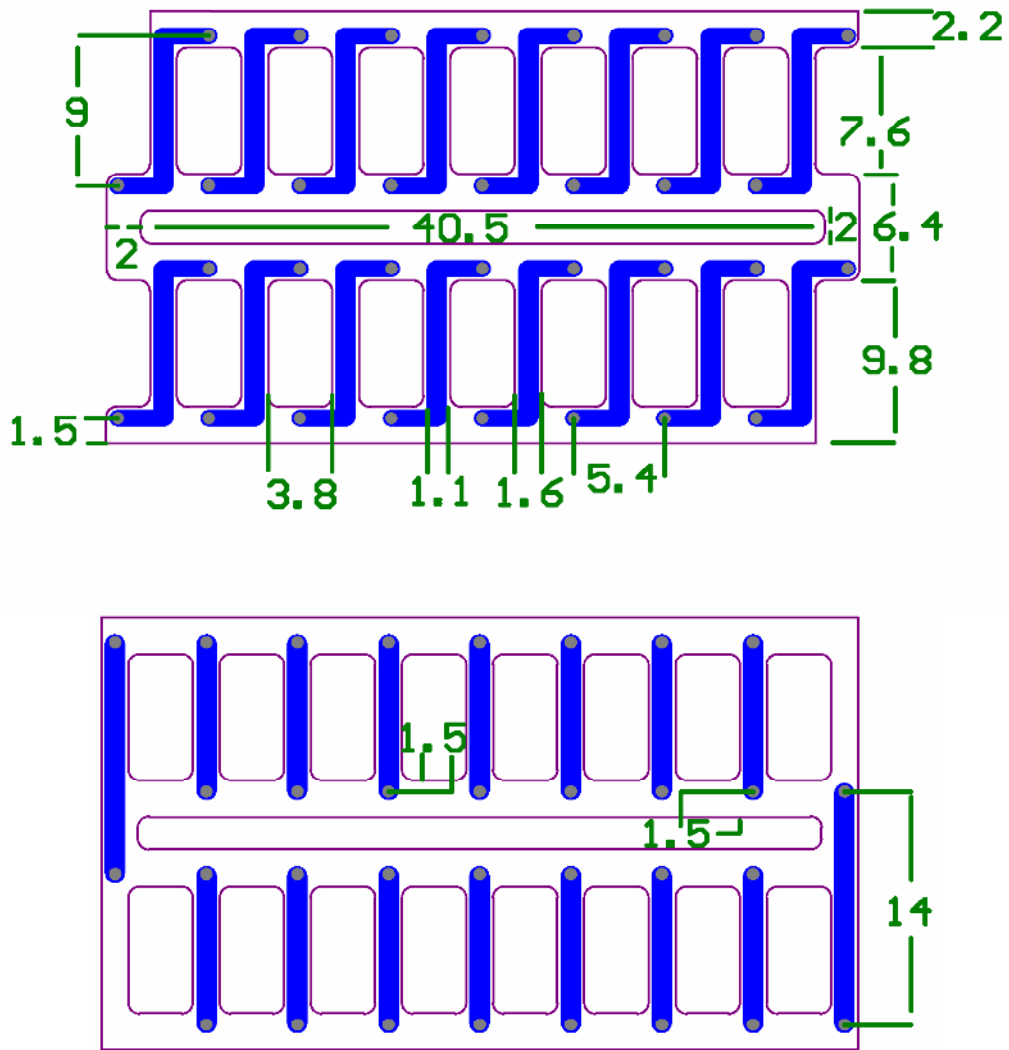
Dimensions du PCBs utilisés pour réaliser les enroulements du composant méandre. Les dimensions sont en mm.
